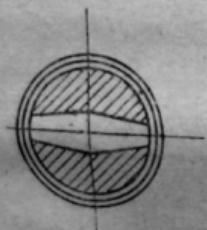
Схема станка для нагартовки обода компенсированных балансов.
